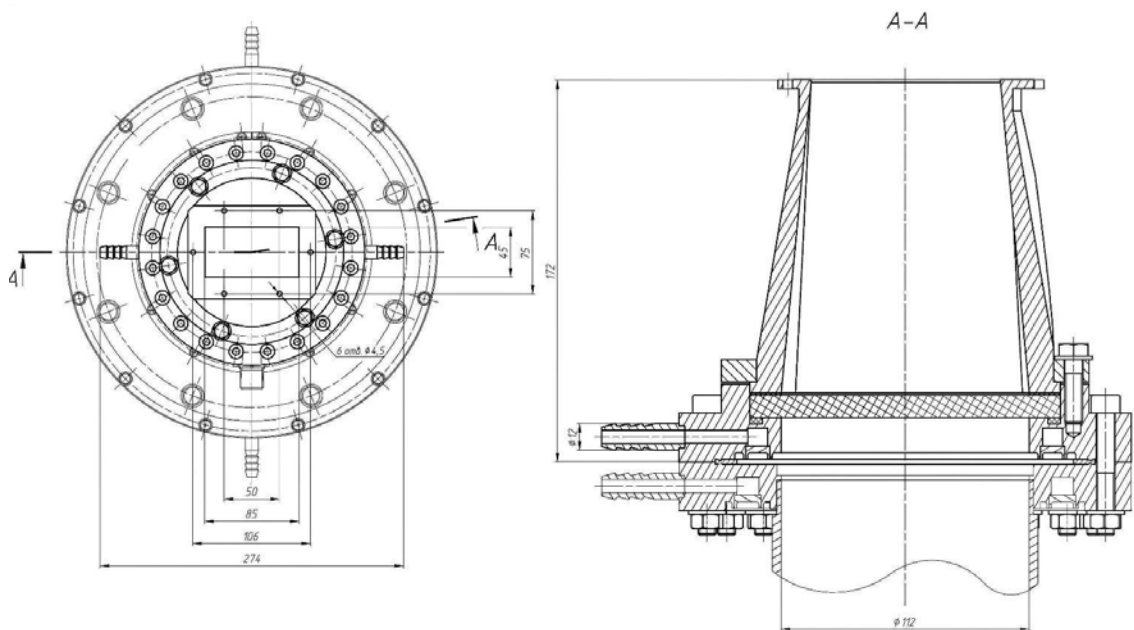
Сборочный чертеж элементов передающей волноводной системы (согласующего рупора) сверхразмерного СВЧ - реактора
